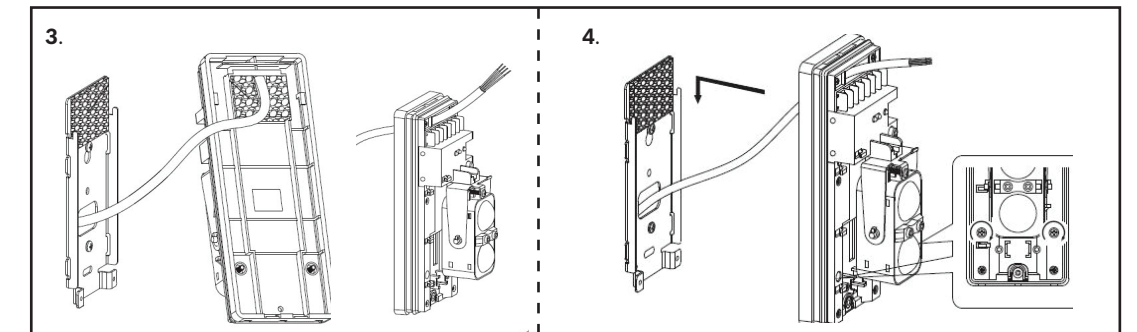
Colocación del cableado y montaje del sensor en la placa de montaje
